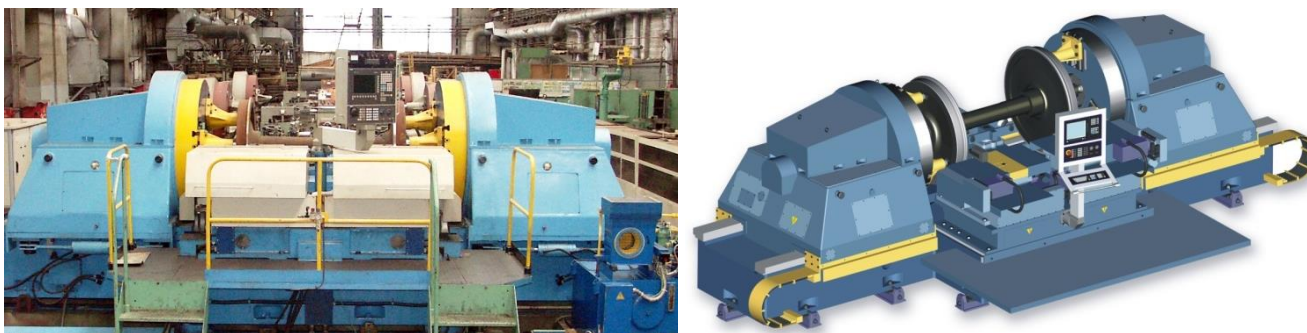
Колесотокарний верстат моделі 1836.10МФ3 з ЧПК
